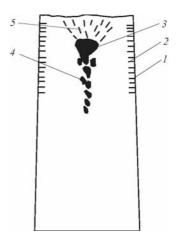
Строение слитка полуспокойной стали: I — наружная корочка слитка; 2 — зона сотовых пузырей; 3 — усадочная раковина; 4 — подусадочная рыхлость; 5 — «мост» плотного металла
